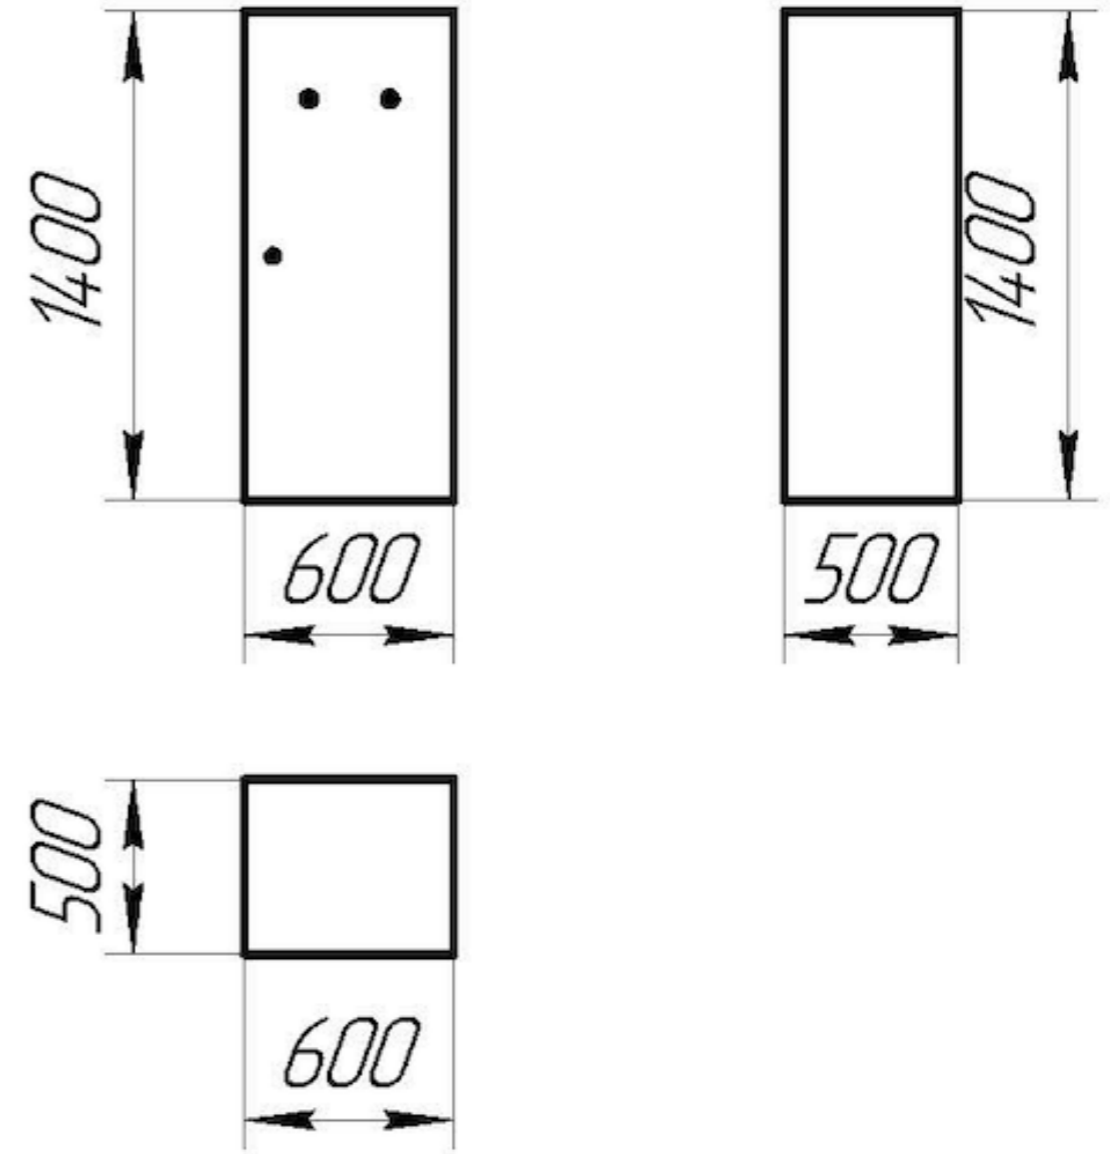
Габаритный чертеж устройства автоматического ввода резерва
